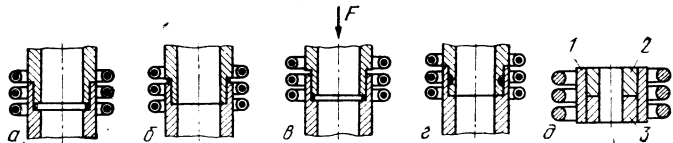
Варианты пайки и расположения индуктора при соединении труб: а — поднимающийся припой; б — опускающийся припой; в — поднимающийся припой со смещением детали; г — с запасом припоя
